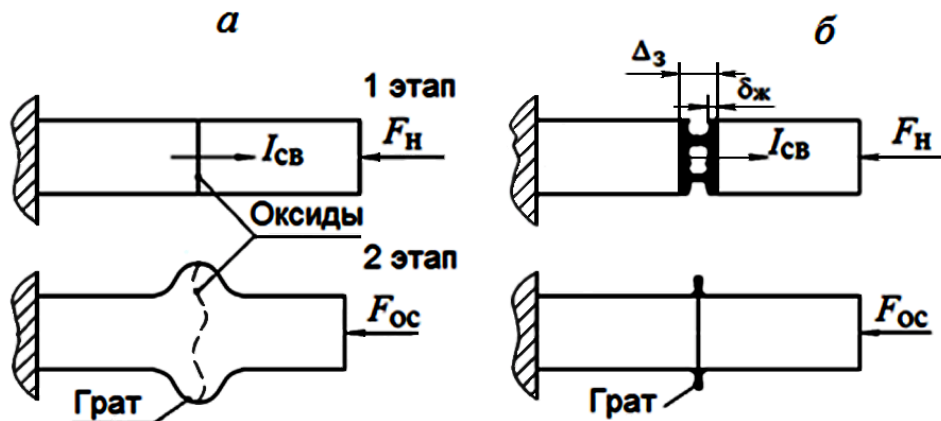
Этапы образования соединений при стыковой сварке:
